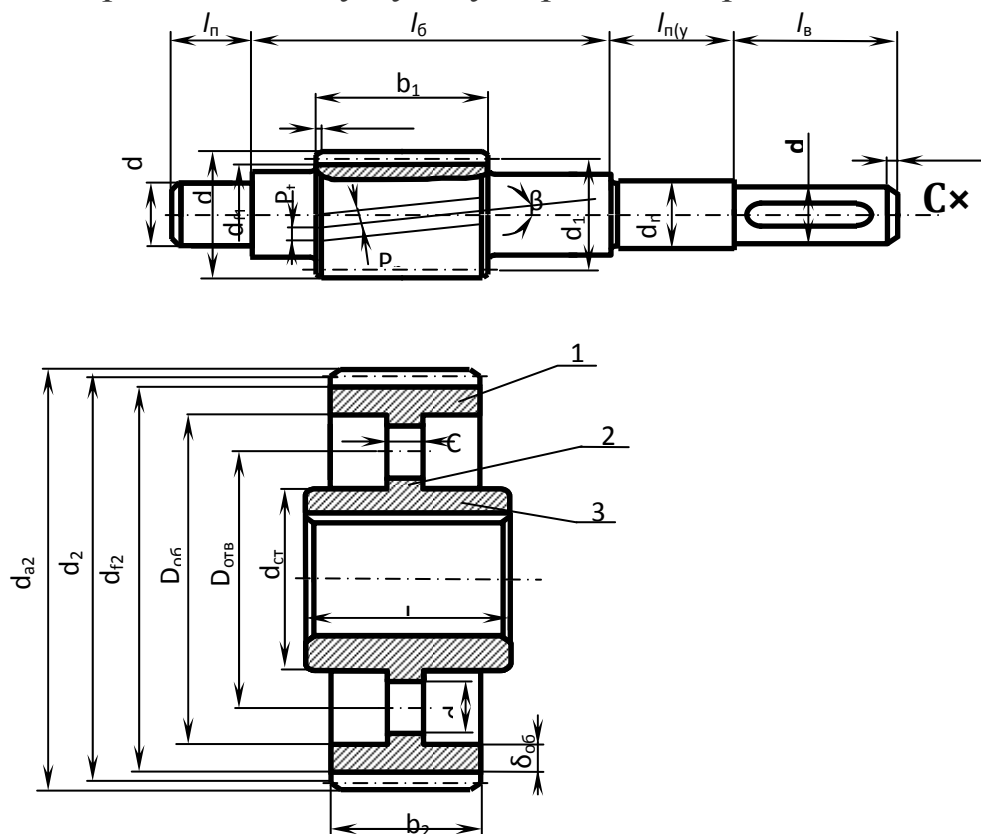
Эскизы вала-шестерни и зубчатого колеса
